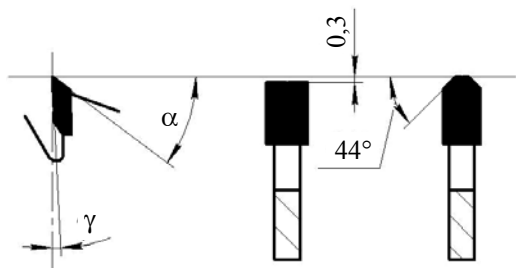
Плоскотрапецевидный профиль зубьев дисковых пил с пластинами твердого сплава для распиловки ламинированных ДСтП
